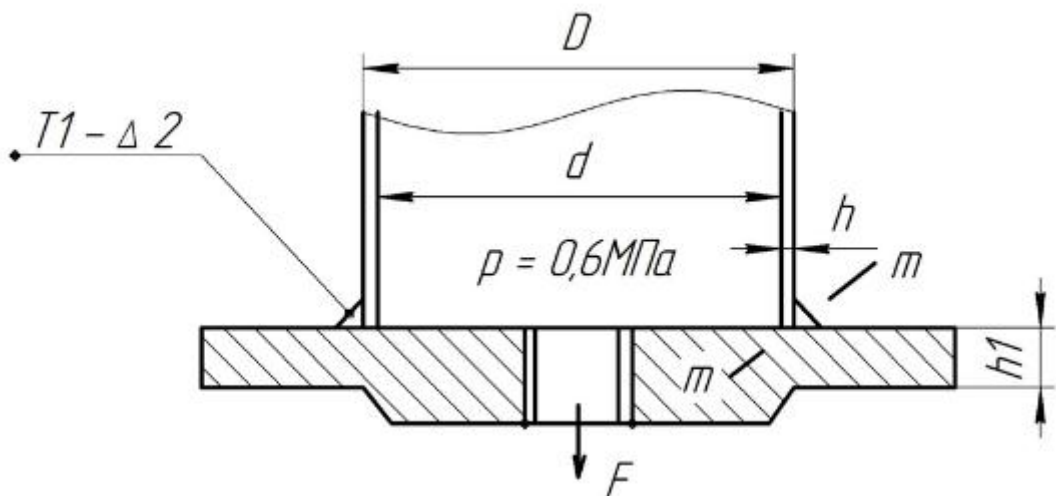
Схема розрахунку зварного з'єднання
